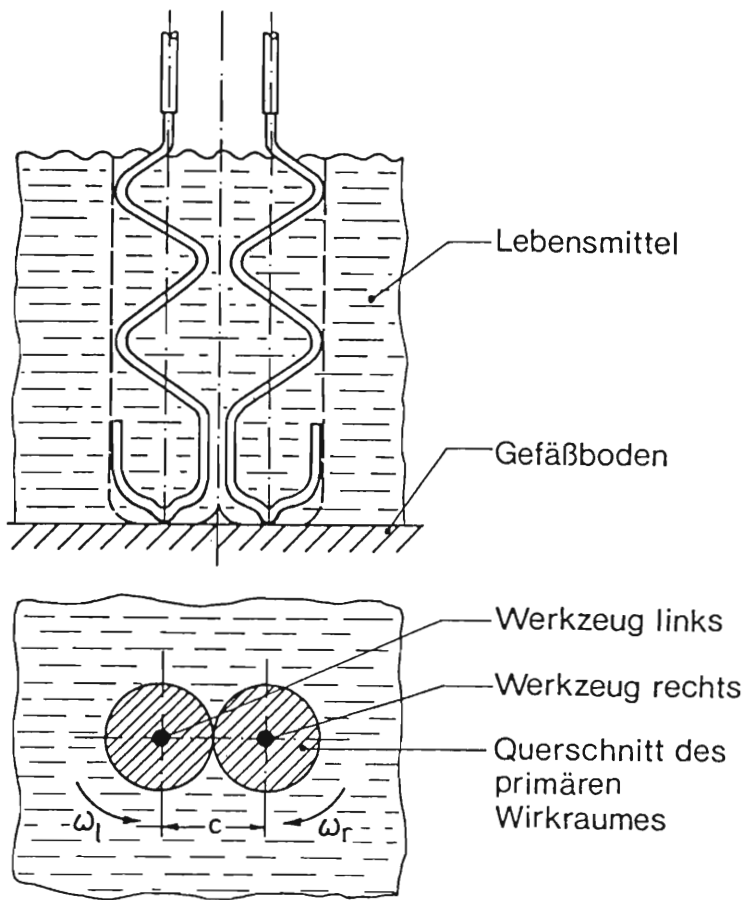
/10: Primärer Wirkraum der Knetwerkzeuge einer Hand-Küchenmaschine
